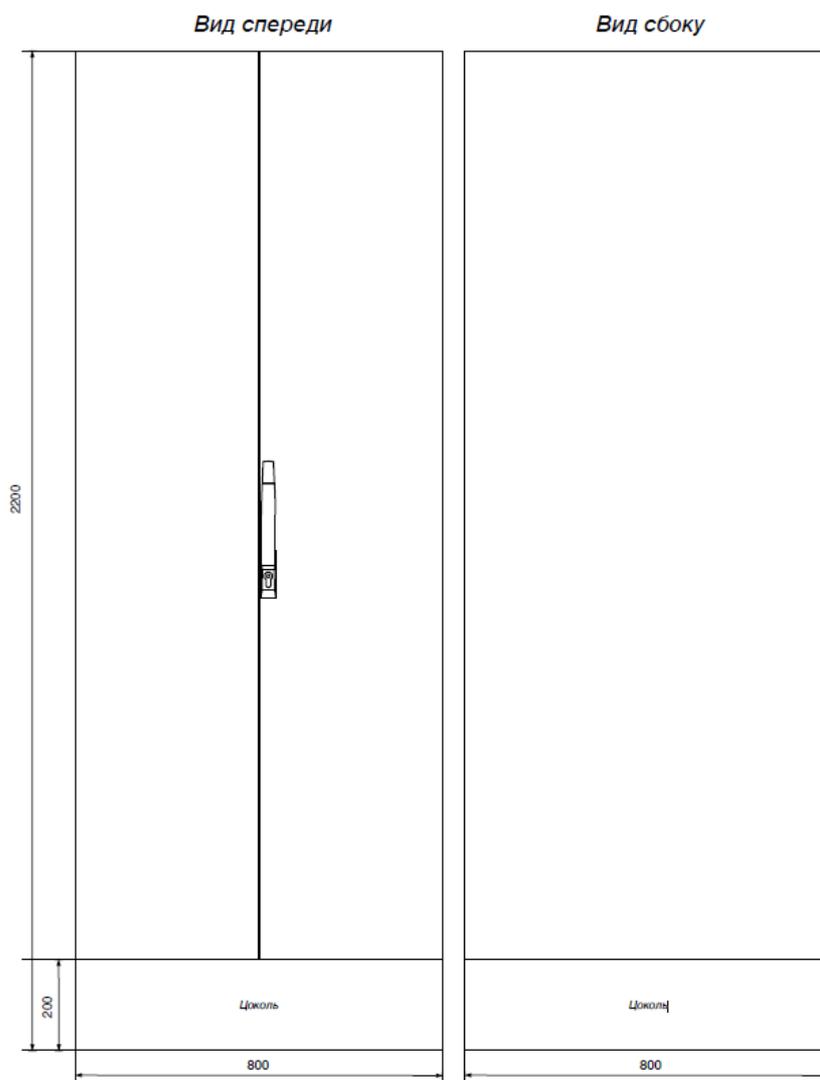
Внешний вид и габаритные размеры концентратора с одностворчатыми дверями
